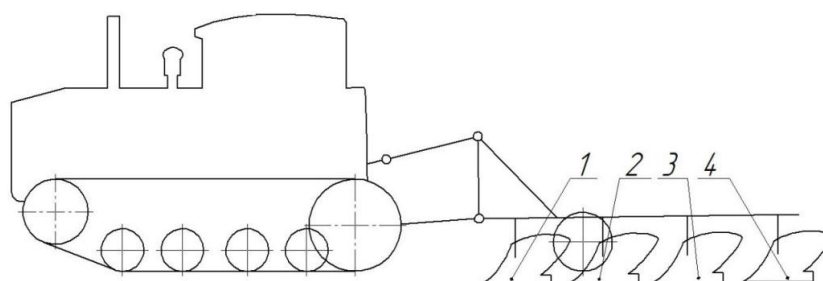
Схема расстановки лемехов на корпусах плуга ПЛН-4-35.
